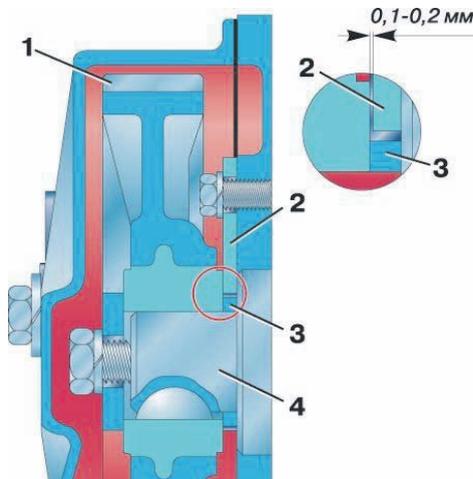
Упорний фланець розподільного валу: 1 – шестерня; 2 – упорний фланець; 3 – розпірне кільце; 4 – розподільний вал.
